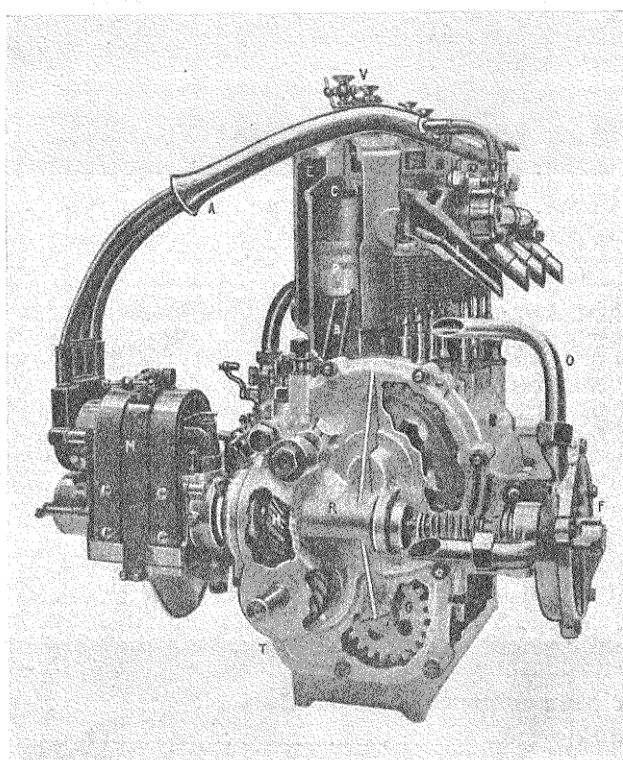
Coupe du moteur 14-chevaux, 4 cylindres, de Dion-Bouton.
